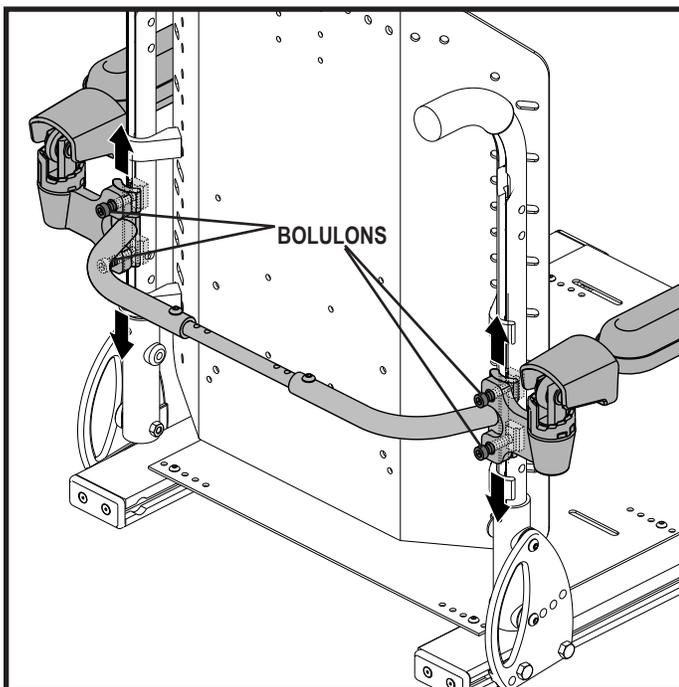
Réglage en hauteur des accoudoirs Cantilever fixée sur la barre
